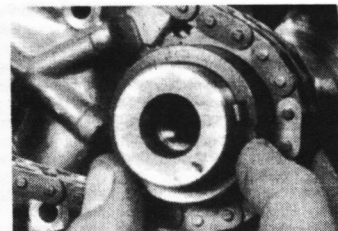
а Установка приводной цепи на звездочку коленвала (отметьте, что метка на звездочке и пластина находятся напротив друг друга)
